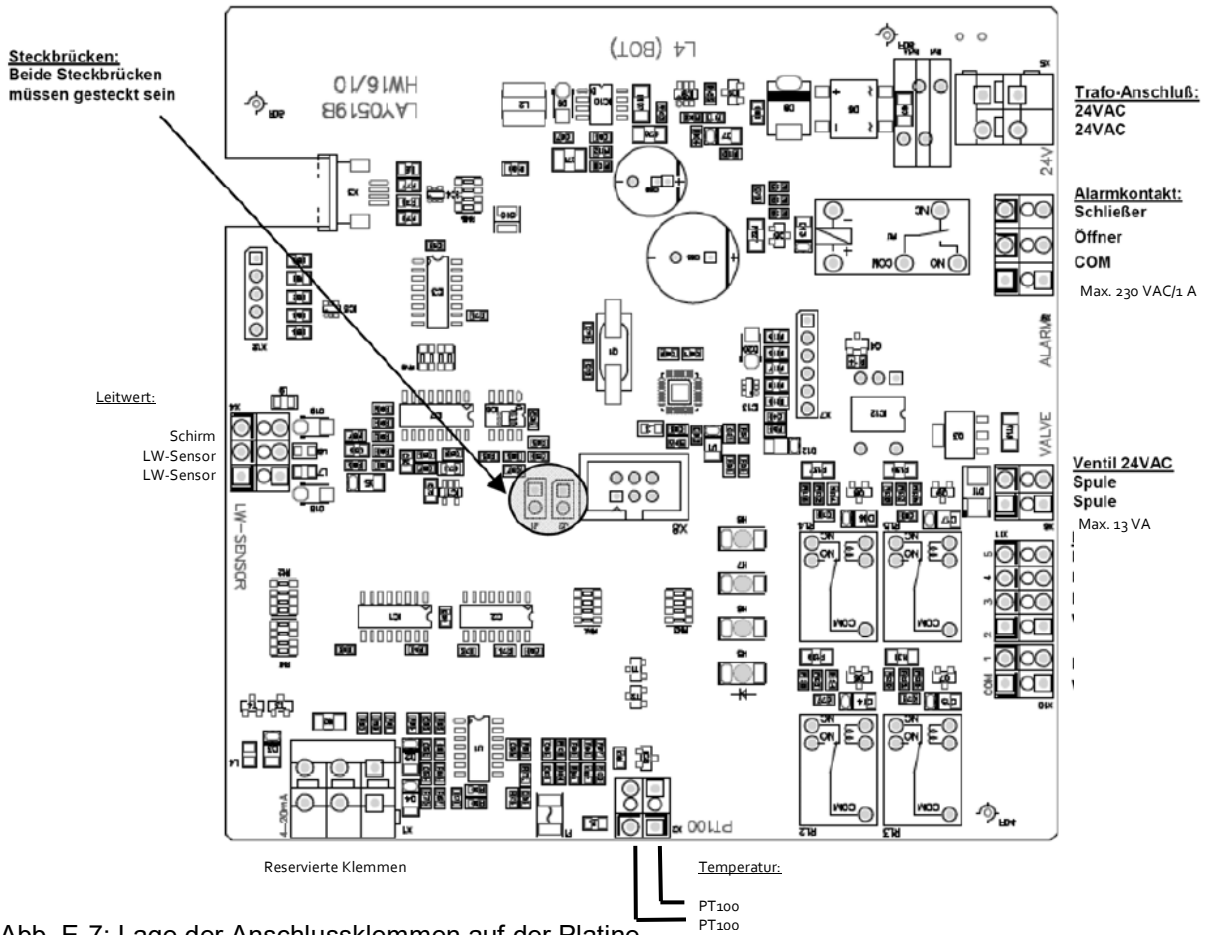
Lage der Anschlussklemmen auf der Platine
